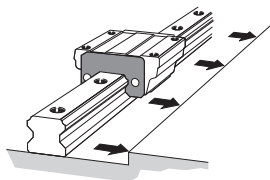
Выравнивание рельса LM относительно базовой поверхности
